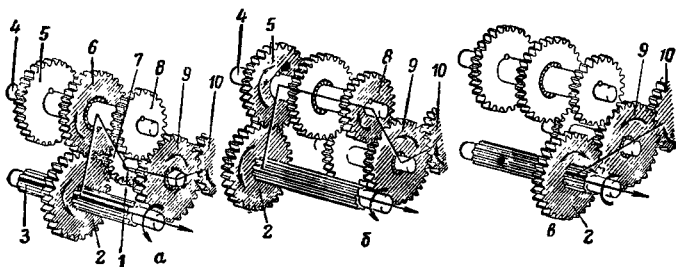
Схема положений шестерен коробки отбора мощности автомобиля ГАЗ-63.
